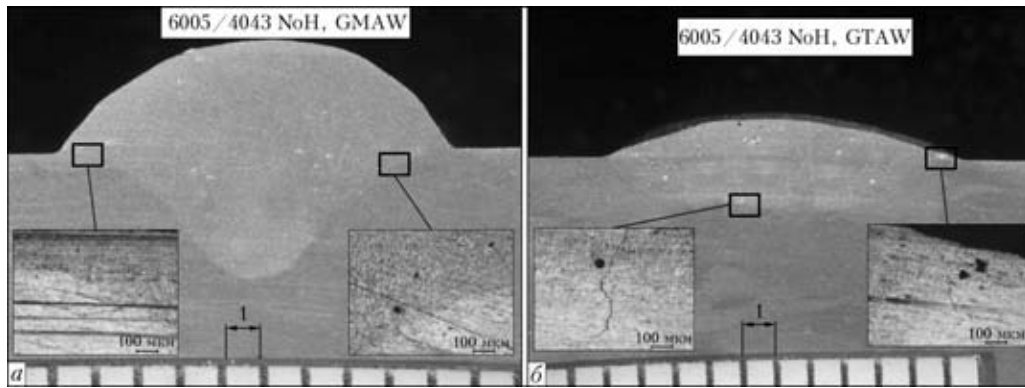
Макрошлифы соединений сплава 6005, выполненных с использованием присадочного металла 4043 без предварительного подогрева способом GMAW (а) и GTAW (б)
